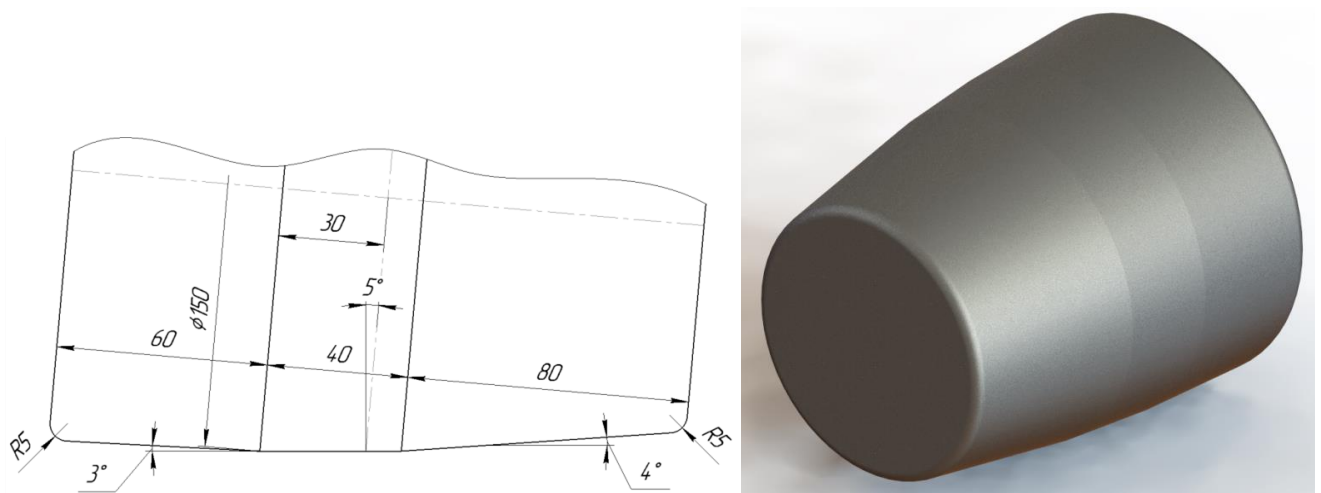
Бочка валка прошивного стана «30-80»
